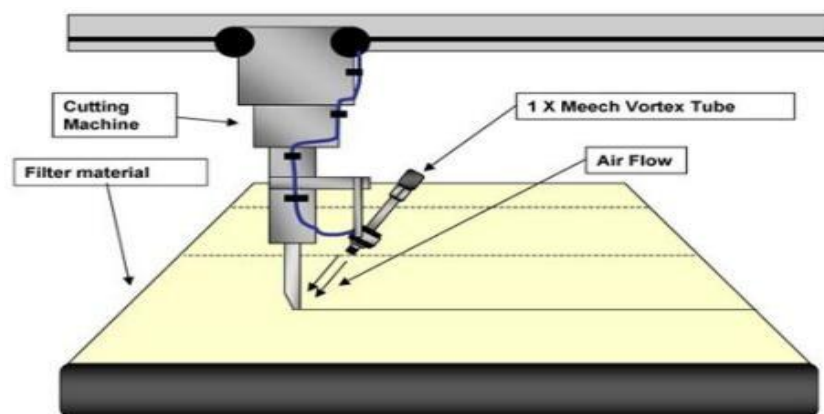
Intégration d'un tube vortex sur une machine de découpage.
